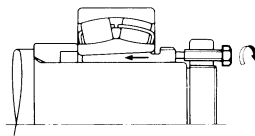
Посадка подшипника на запрессовываемой втулке
